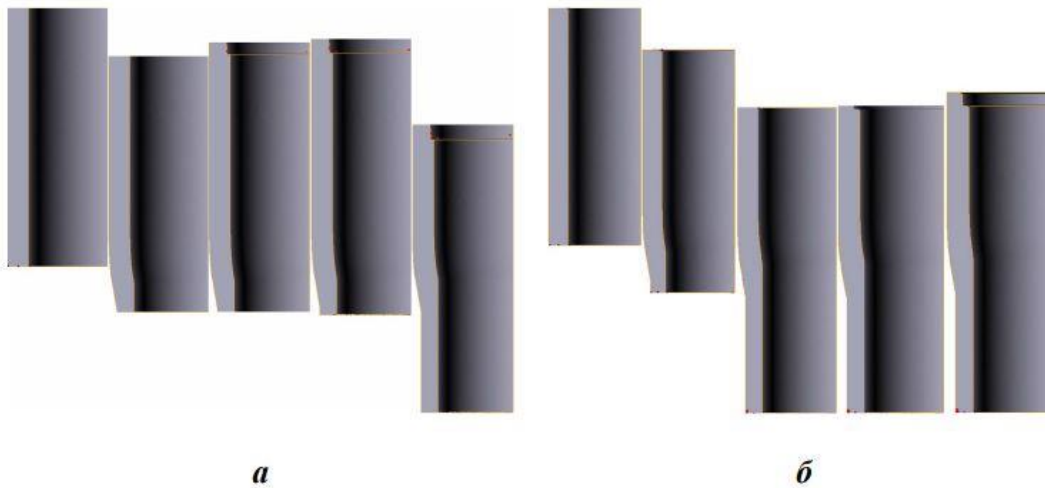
Заготовка на етапах деформування при суміщенні операцій обтиску із потоншенням та видавлювання трубчастих заготовок.
